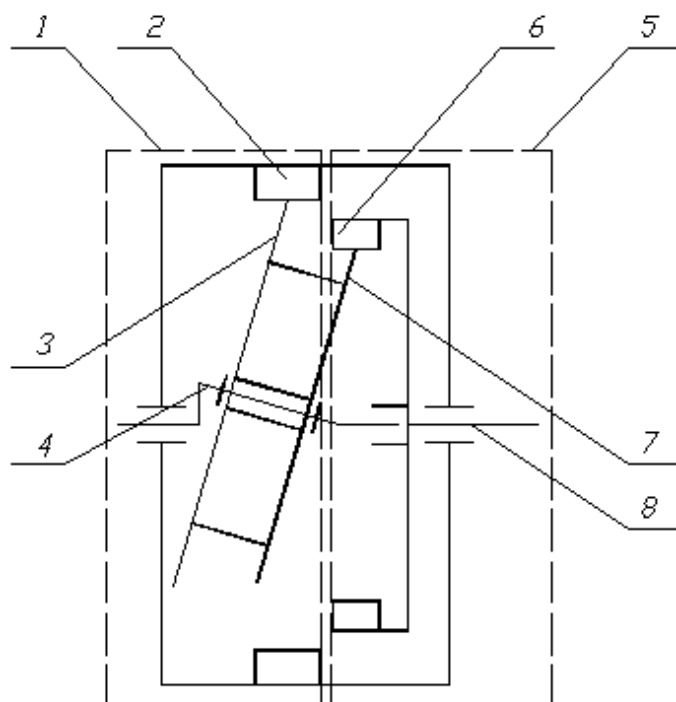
Структурная схема ППП с двумя зубчатыми венцами
